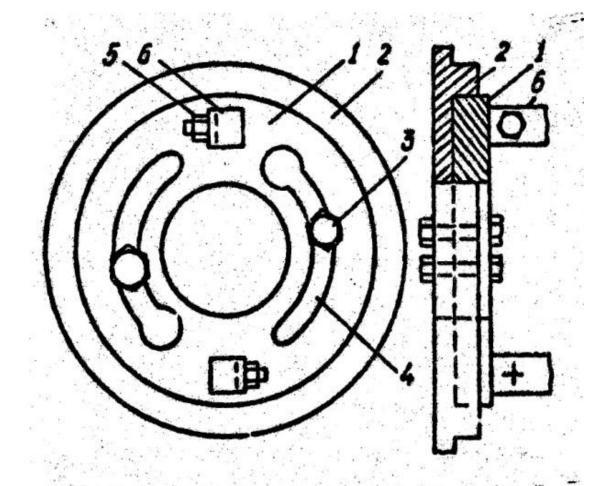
Щеточное устройство: I - траверса; 2 - подшипниковый щит; 3 - болт крепления траверсы; 4 - прорезь; 5 - болт крепления пальца щеткодержателя; 6 - палец щеткодержателя
